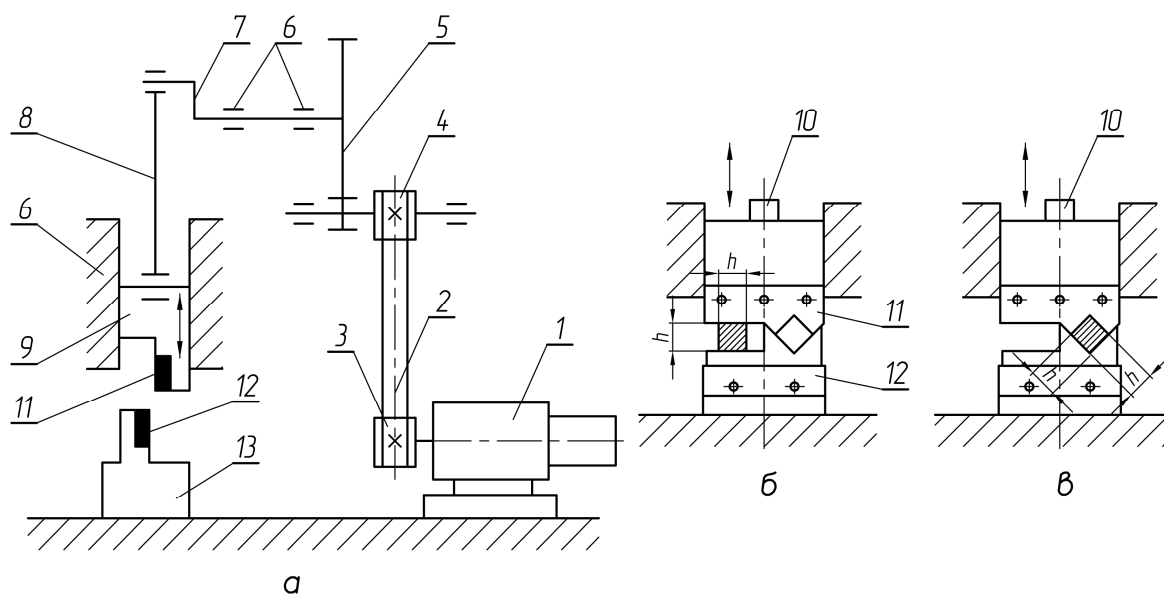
Кинематическая схема установки ножниц (а), положение квадратной заготовки при ее разделении параллельными (б) и фасонными (в) ножами
